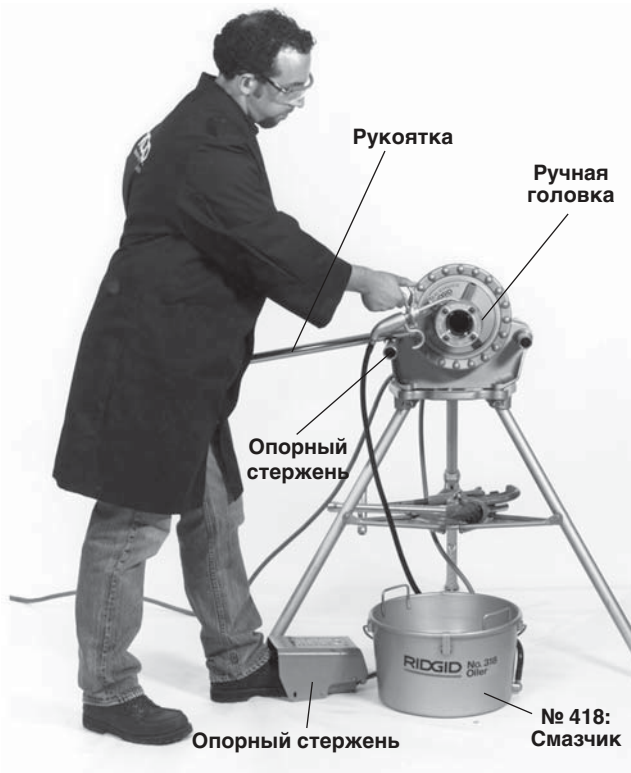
Нарезание резьбы с помощью ручной головки
